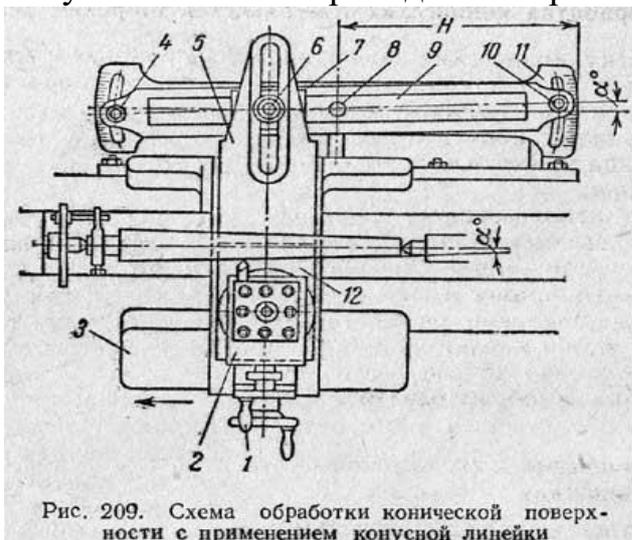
Схема обработки конической поверхности с применением конусной линейки
